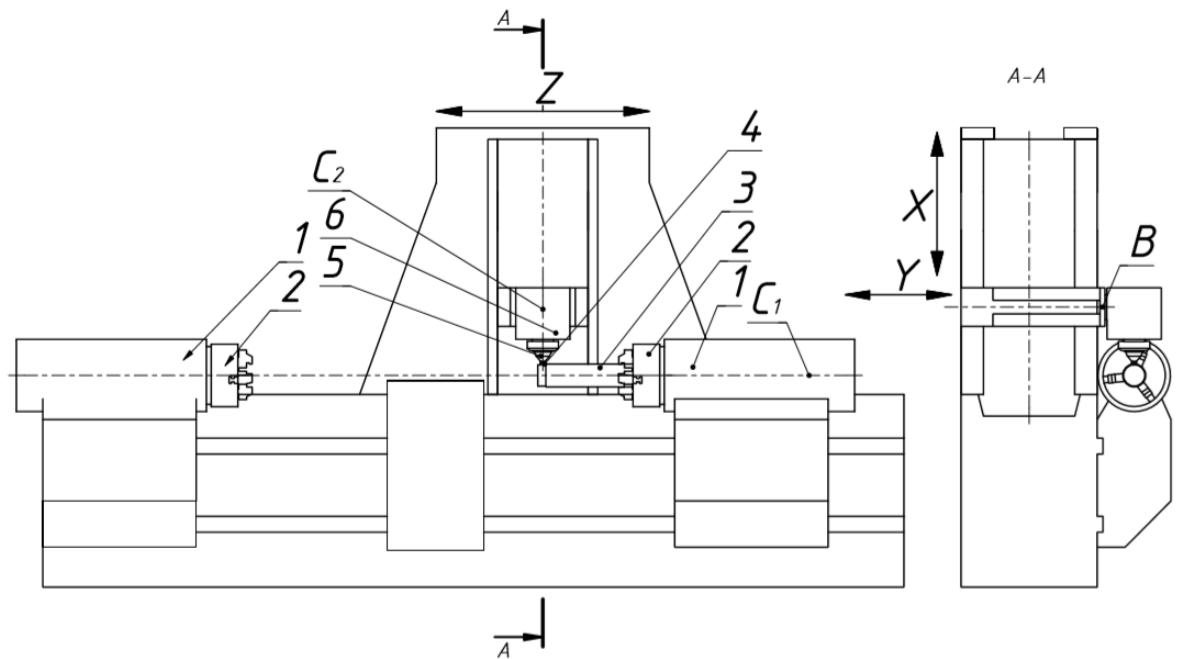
Схема токарно-фрезерного верстата з ЧПК
